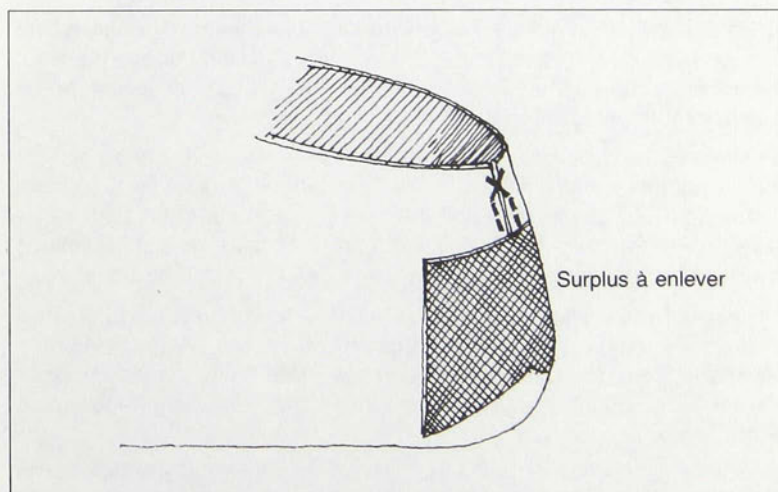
En relevant la partie pendante obtenue par la coupe en diagonale, on découvre le surplus de cuir à enlever pour terminer le cintrage arrière.
